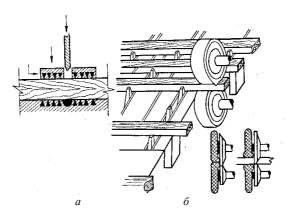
Схема торцовки досок с помощью ножевых приспособлений: a – установка позиционная; δ – установка проходного типа
